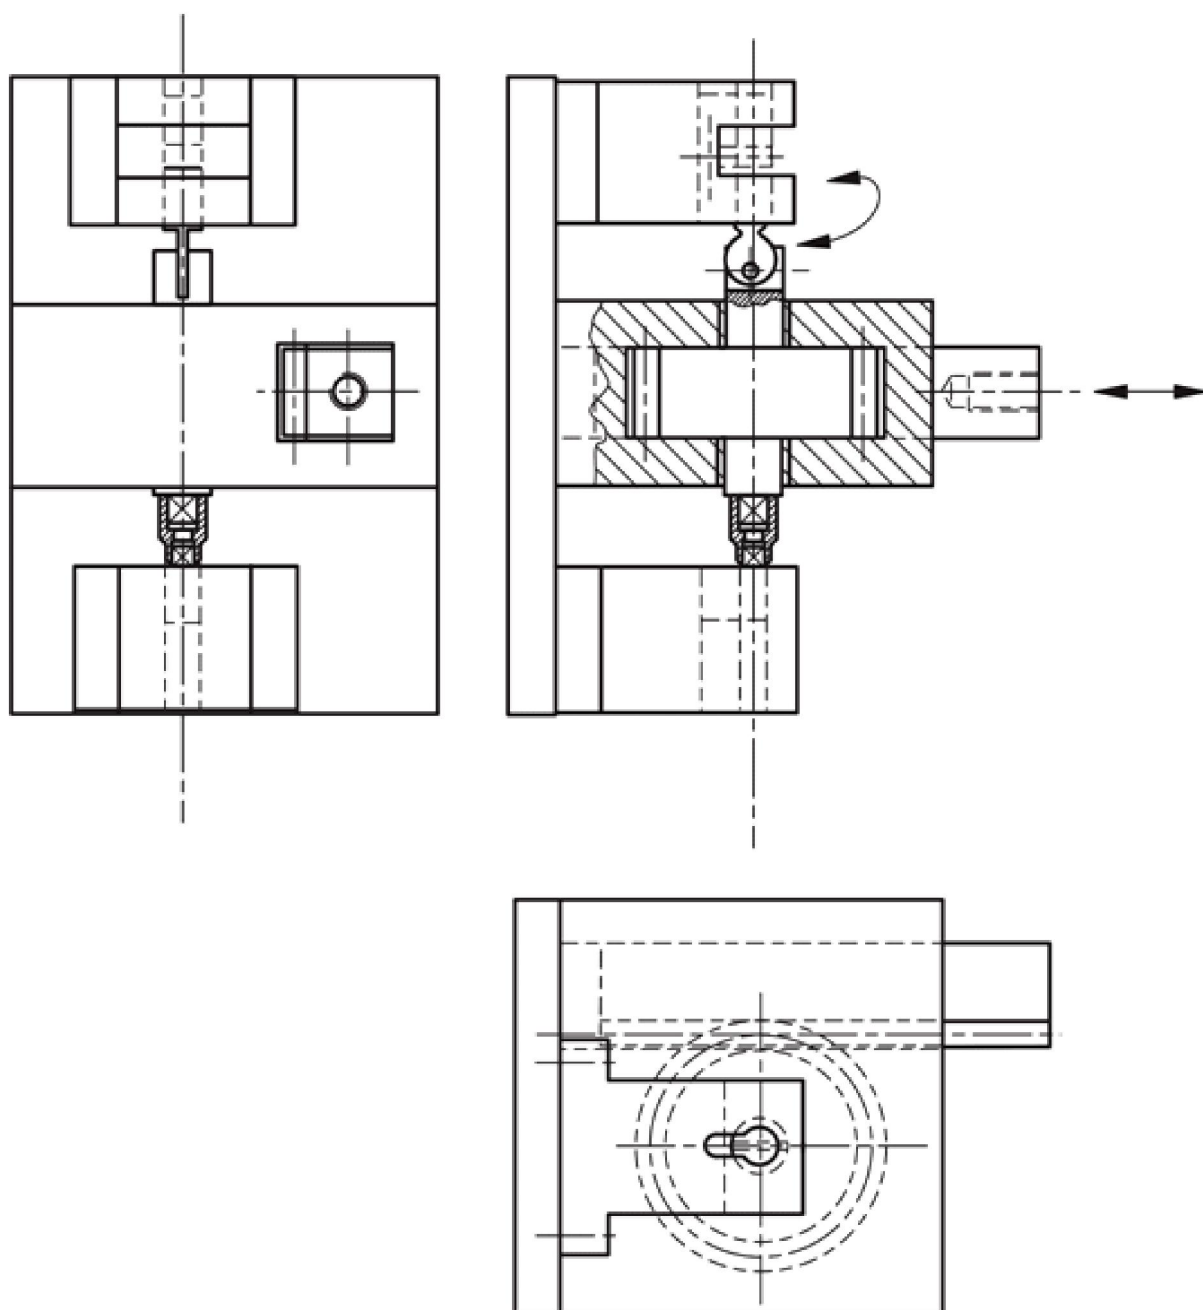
Металлическое приспособление для испытания устойчивости к вытягиванию ротора цилиндра/цилиндрического механизма.
